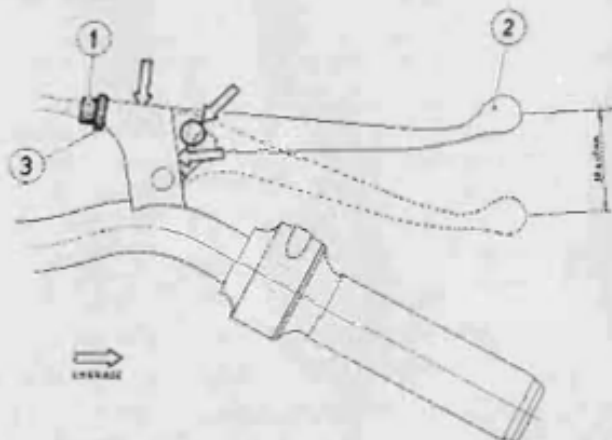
Mando freno delantero: Reglaje y engrase.
